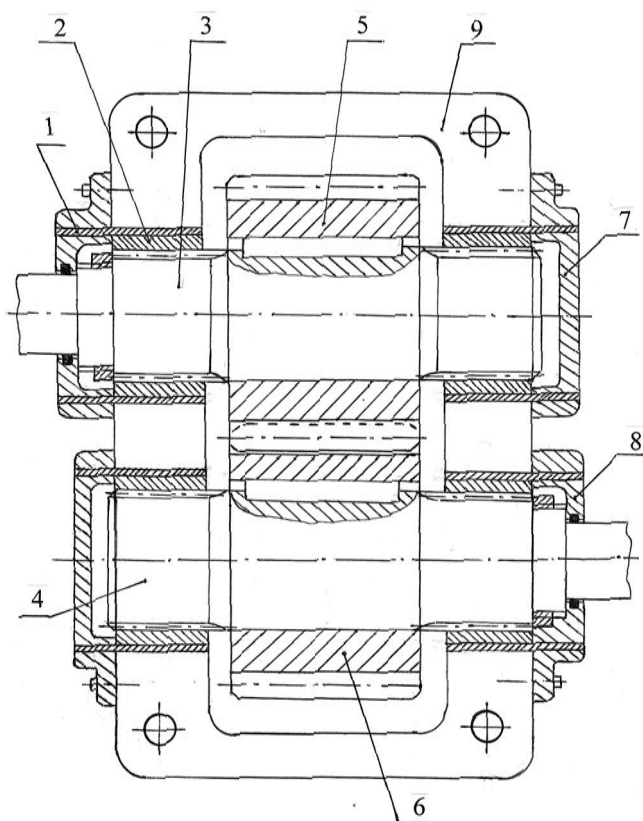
Трибосистема (редуктор): 1, 2 – втулки подшипника скольжения; 3, 4 – валы; 5, 6 – зубчатые колеса; 7, 8 – крышки; 9 – корпус
